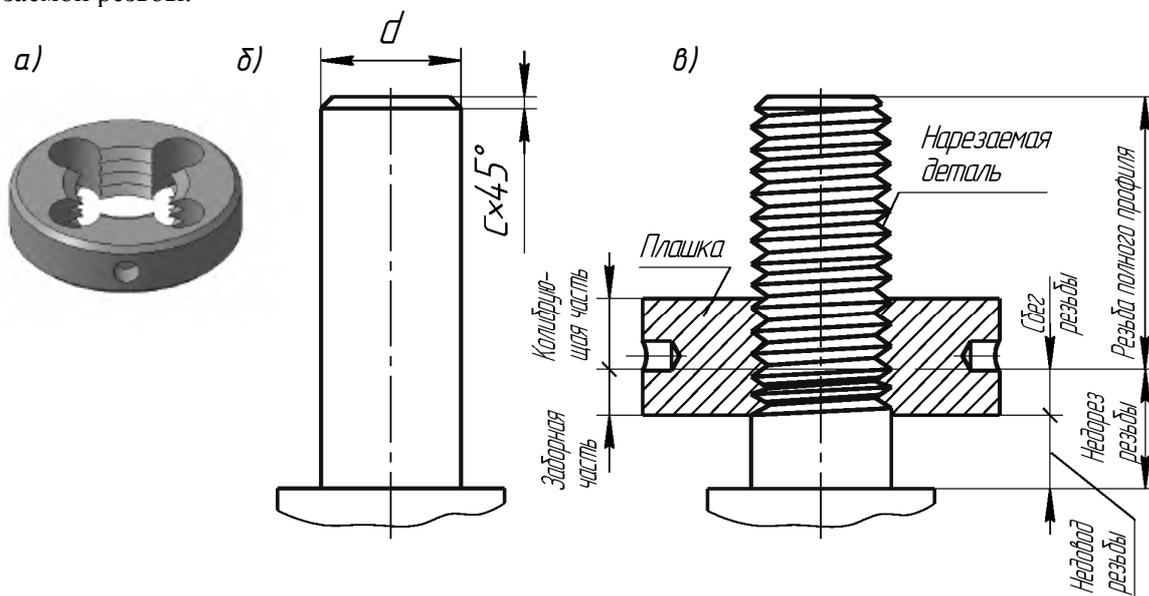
Нарезание наружной цилиндрической резьбы:
